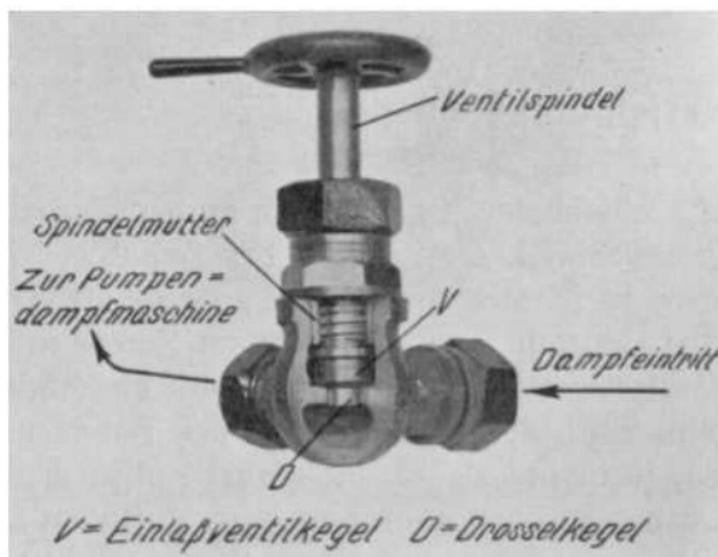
Anlaßventil für Luft- und Fahrpumpe
